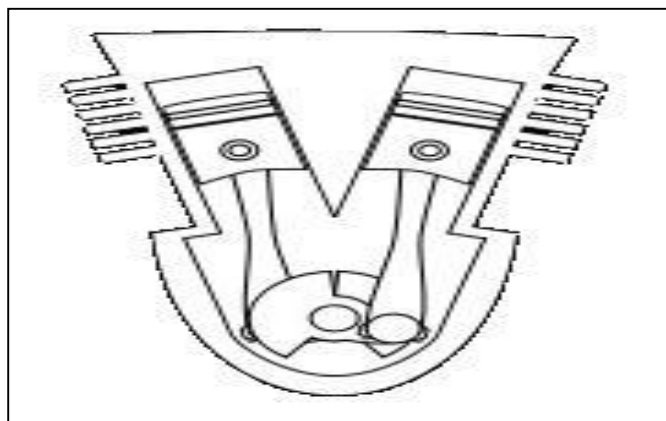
MOTOR EN VR DE 2 CILINDROS
